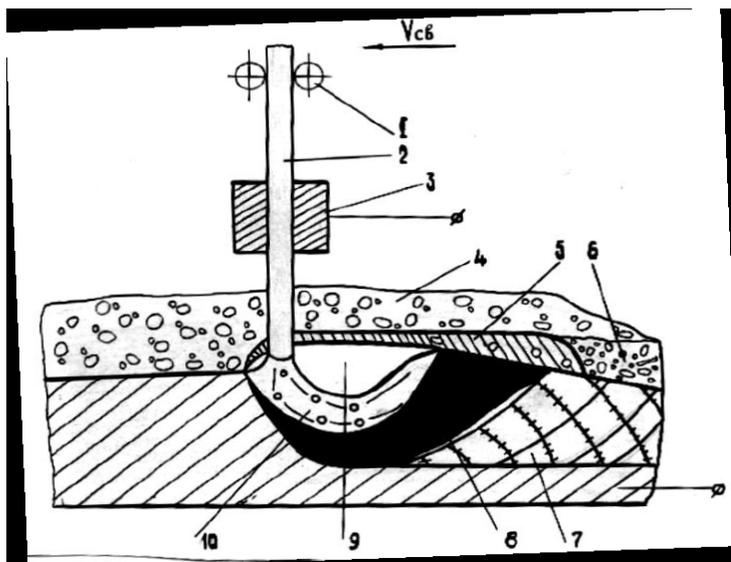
Схема автоматической сварки под слоем флюса: 1 – подающие ролики; 2 – электродная проволока; 3 – токоподвод; 4 – флюс; 5 – слой расплавленного флюса; 6 – шлаковая корка; 7 – сварной шов; 8 – сварочная ванна; 9 – газовый пузырь; 10 – дуга
